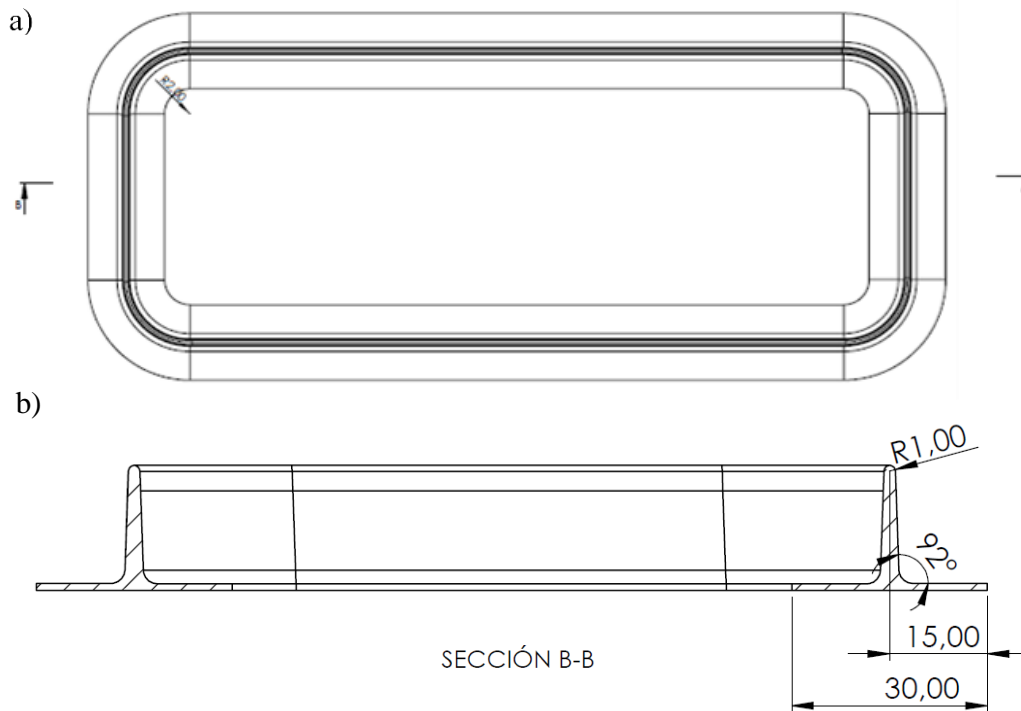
Diseño de preforma 3D para sobremoldeo; a) vista en planta y b) sección transversal.
